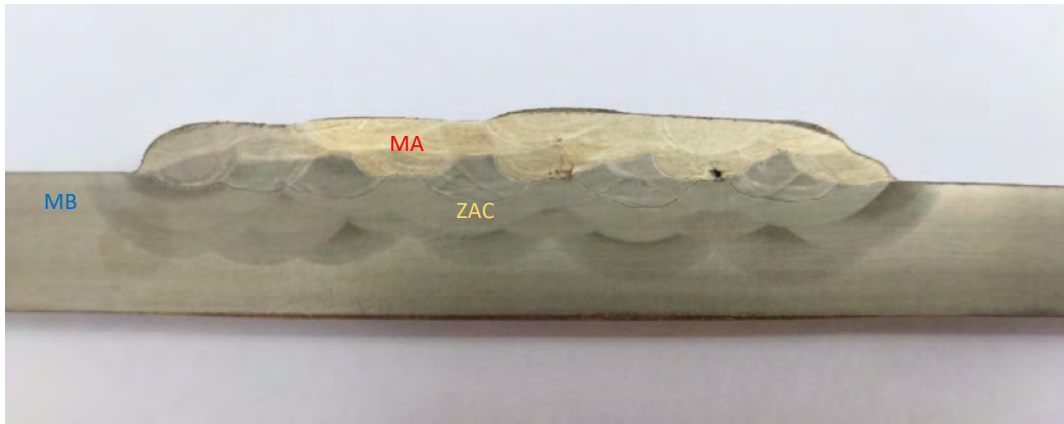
Macrografía de cupón de soldadura sometido a PWHT.
